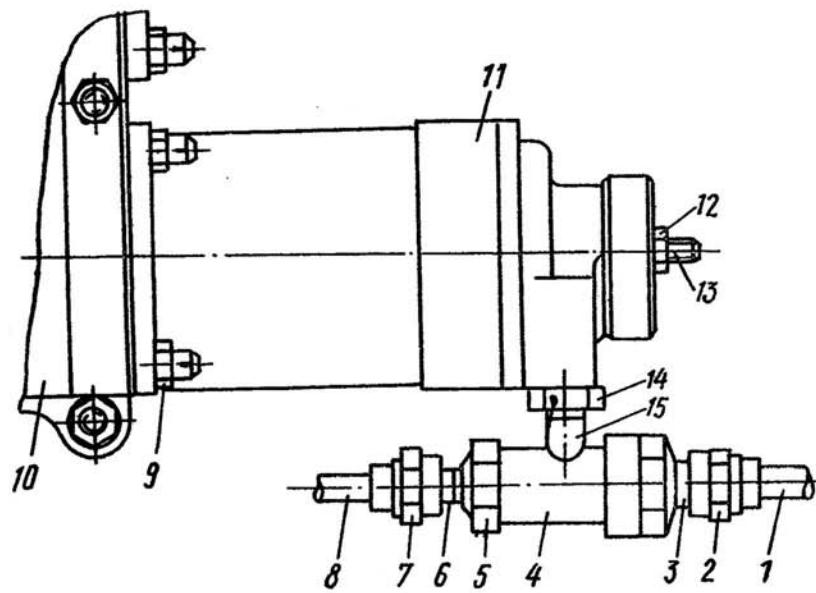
Установка тормоза гидропривода закрылков:
